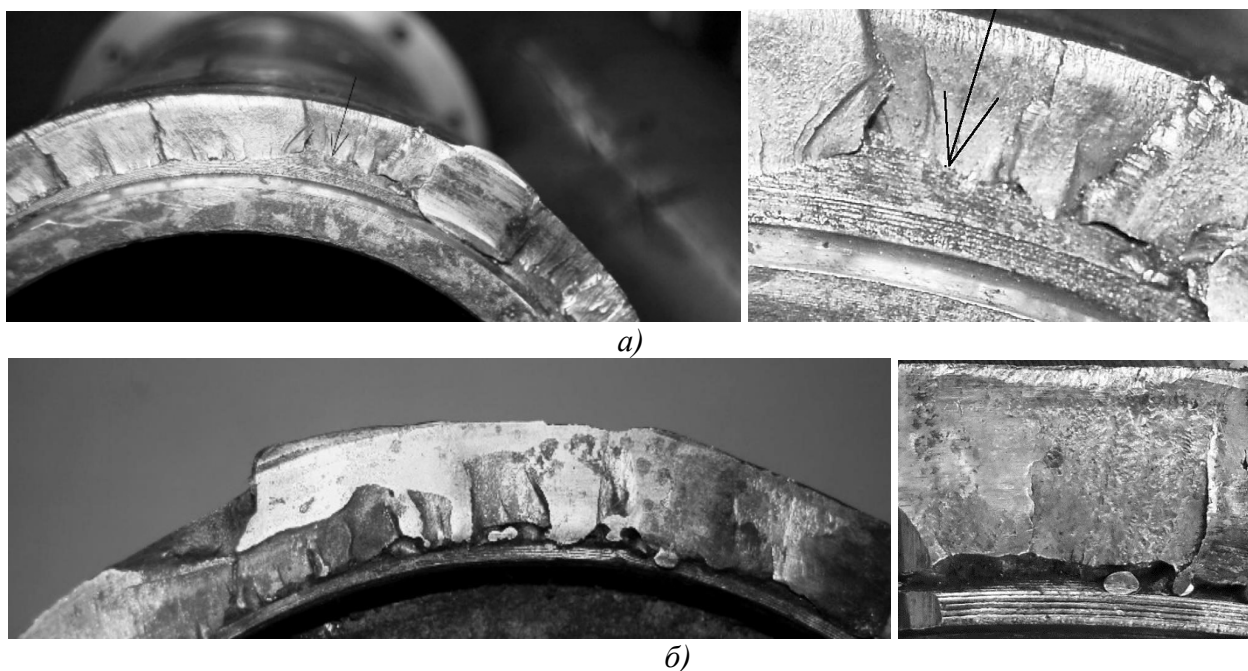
Наружный вид поверхности разрушения: а – вала, б – шлицевой втулки
